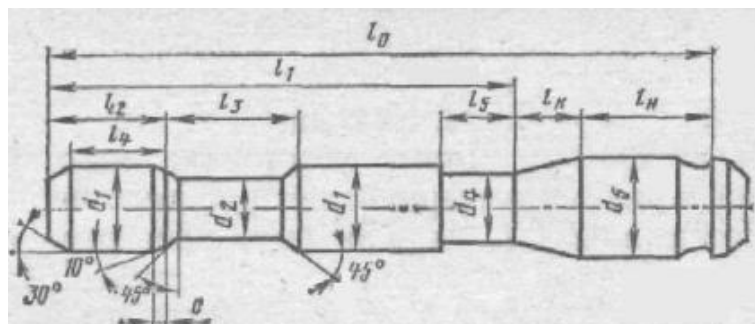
Хвостовик протяжки под быстросменный автоматический патрон
